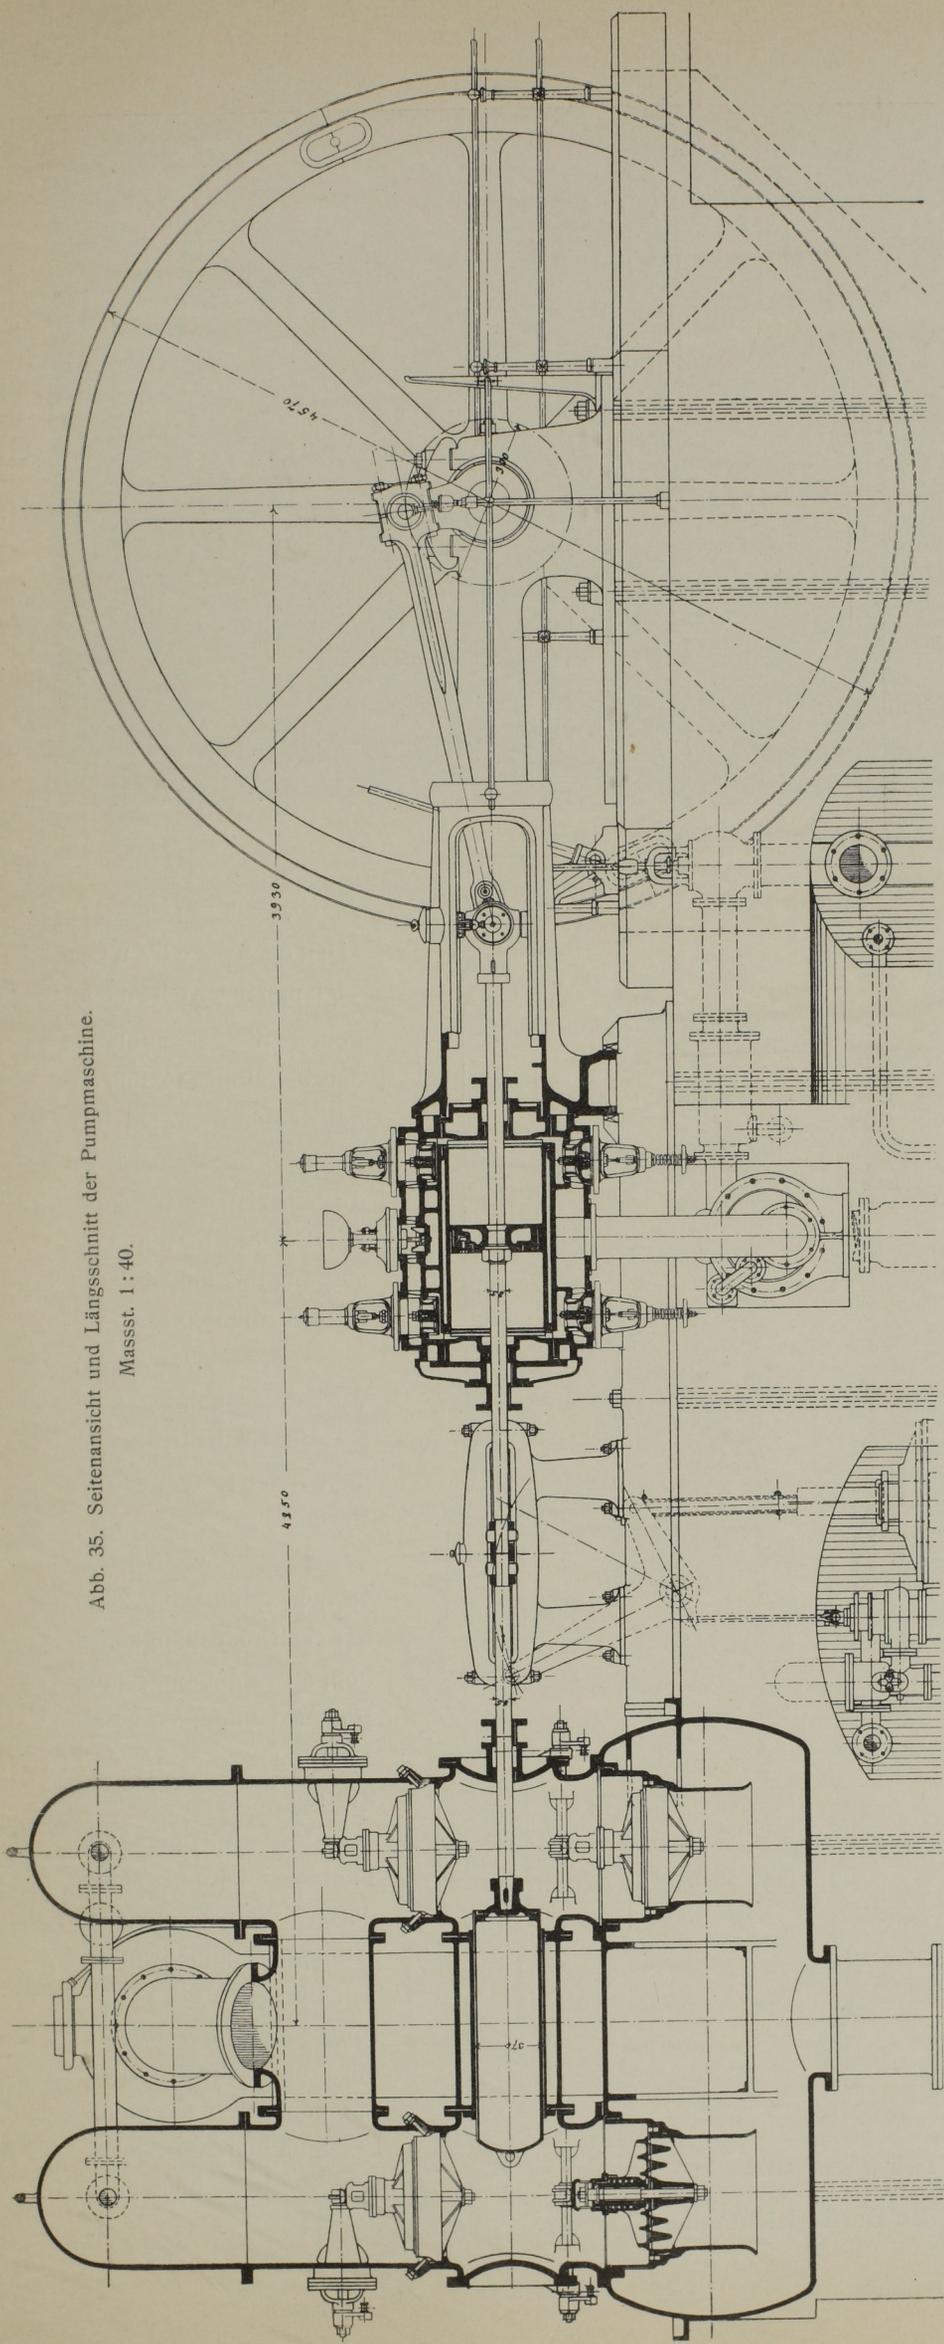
Seitenansicht und Längsschnitt der Pumpmaschine.
